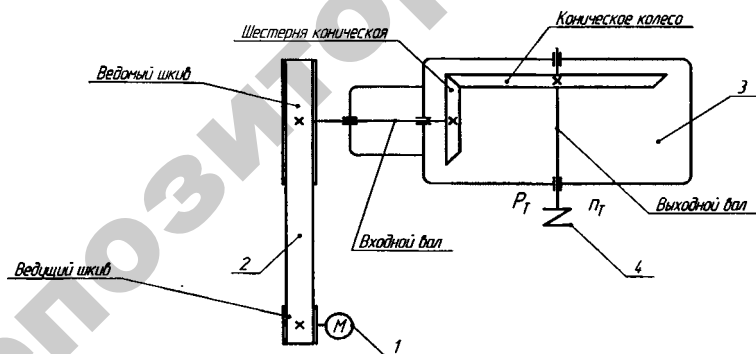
Кинематическая схема привода с коническим редуктором
